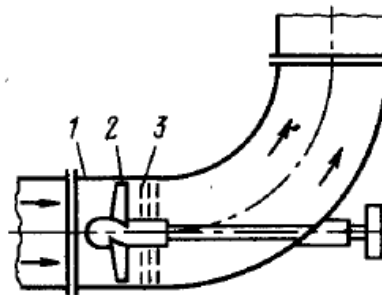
Схема лопатевої турбіни осьового типу: 1 – корпус; 2 – лопать; 3 – лопатевий відвід (направляючий апарат)
